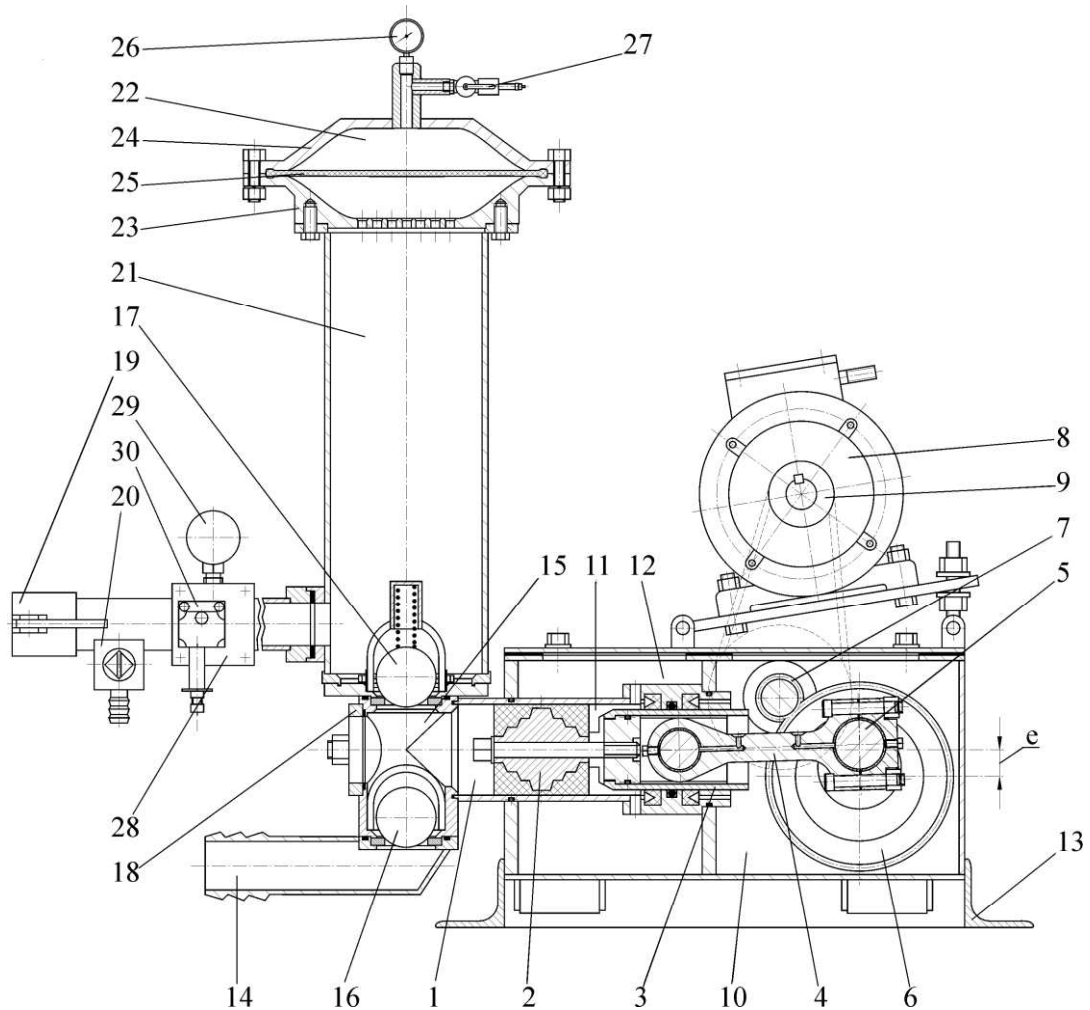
Схема однопоршневого розчинонасосу з компенсатором пульсації тиску: 1 – робочий циліндр; 2 – поршень; 3 – повзун; 4 – шатун; 5 – вісь колінчастого вала; 6 – зубчате колесо; 7 – вал-шестерня; 8 – електродвигун; 9 – клинопасова передача; 10 – камера редуктора; 11 – штокова порожнина; 12 – камера замкнена промивочна; 13 – рама; 14 – патрубок усмоктувальний; 15 – робоча камера; 16, 17 – всмоктувальний та нагнітальний кульовий клапан; 18 – кришка до робочої камери; 19 – нагнітальний патрубок; 20 – з краном зниження тиску; 21 – циліндрична камера; 22 – замкнена камера; 23, 24 – нижня і верхня деталі тарілчастої форми; 25 – гумотканинна діафрагма; 26 – манометр; 27 – ніпель; 28 – діафрагмова камера; 29 – манометр; 30 – реле тиску.
